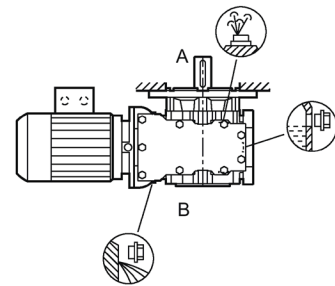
Einbaulagen für Stirnradschneckengetriebe CF Flanschausführung und CAZ mit Gehäuseflansch, Baugröße 39A
